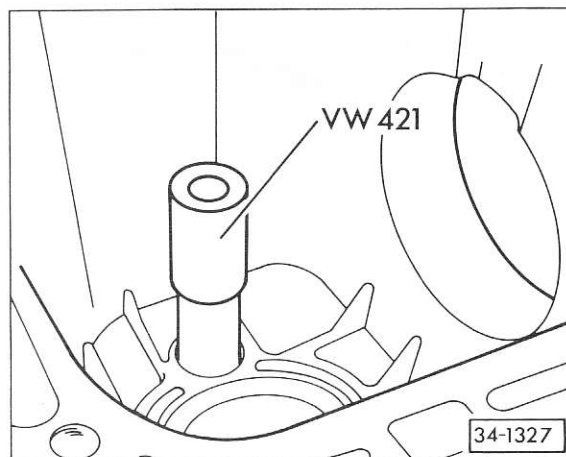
Roulement à aiguilles: extraction du carter de BV
